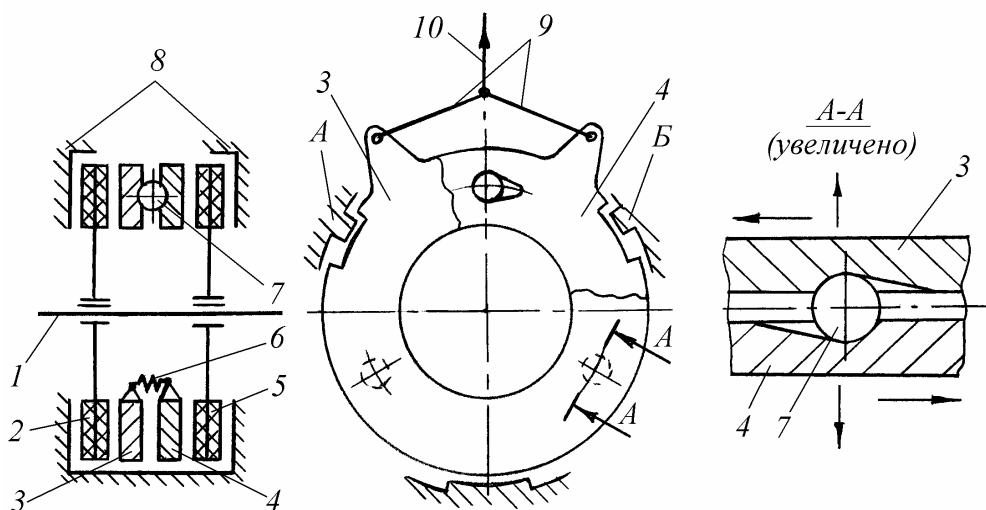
Схема закрытого дискового тормоза с сервоусилением:
